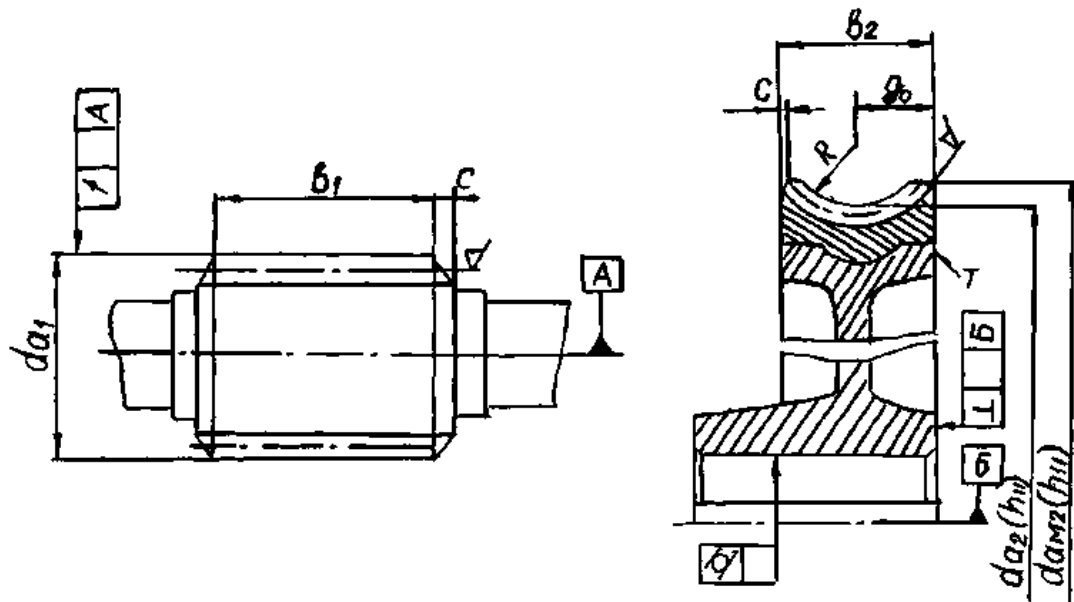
Параметры зубчатых венцов червячной передачи, указываемые на чертежах
